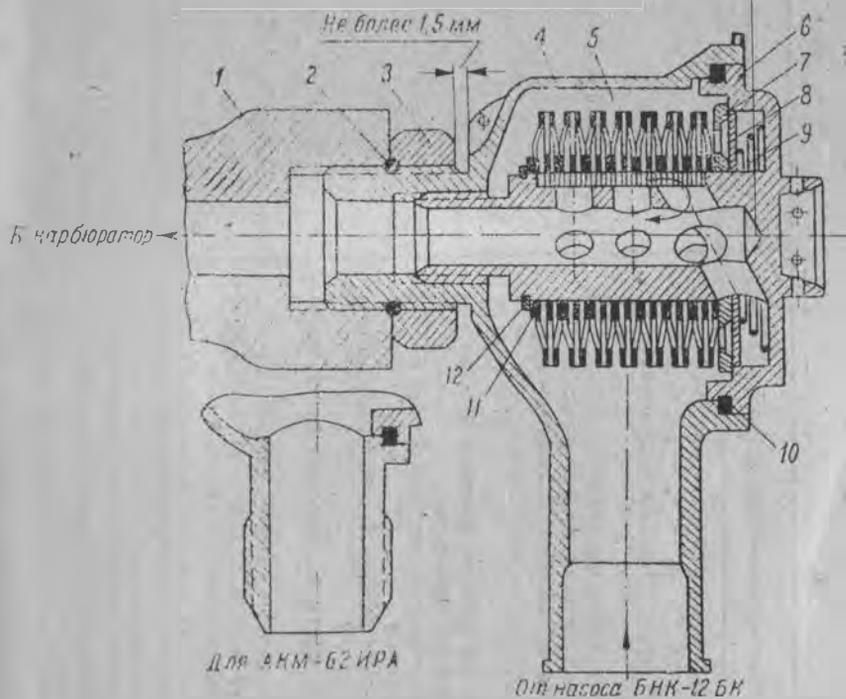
Фильтр тонкой очистки карбюратора: 1 — корпус карбюратора; 2 — резиновое кольцо; 3 — гайка; 4 — корпус фильтра; 5 — фильтр сетчатый; 6 — крышка корпуса; 7 — диск; 8 — клапан; 9 — пружина; 10 — резиновое кольцо; 11 — шайба; 12 — стопорное кольцо
